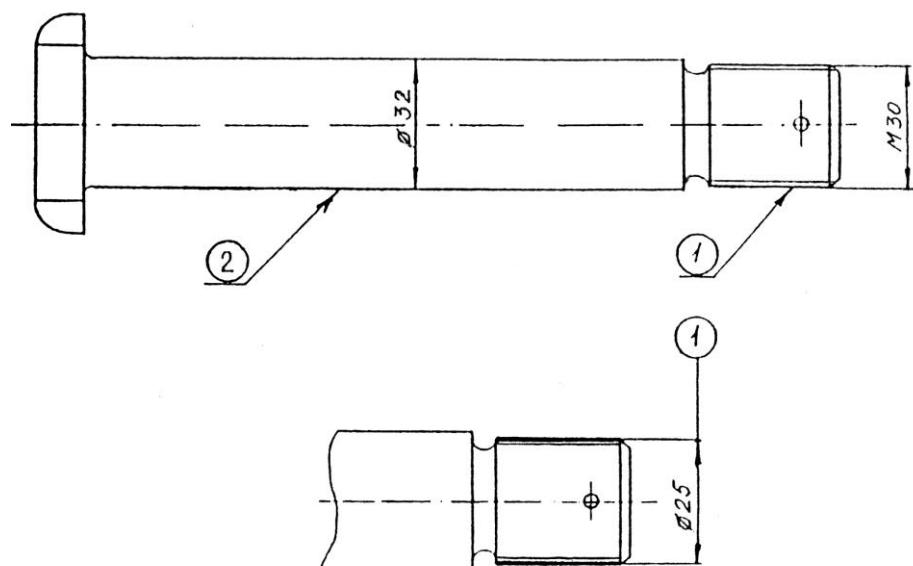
Основные дефекты болта гасителя колебаний, ремонтируемые сваркой или наплавкой
